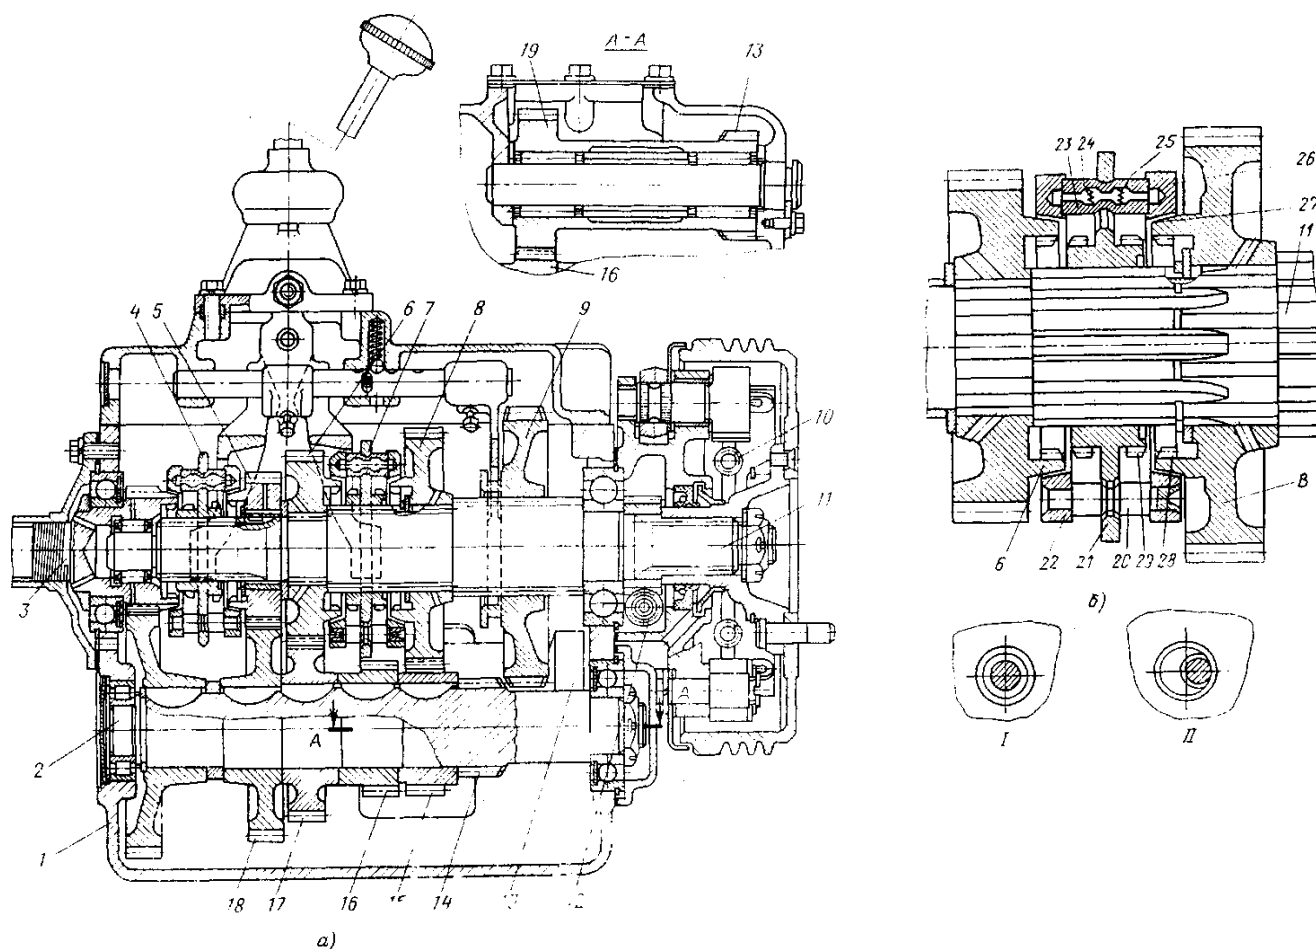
Коробка передач автомобиля ЗИЛ-130: а – общий вид; б – синхронизатор; 1 – картер; 2 – промежуточный вал; 3 – ведущий вал; 4 и 7 – синхронизаторы; 5 и 18 – зубчатая пара четвертой передачи; 6 и 17 – зубчатые колеса третьей передачи; 8 и 15 – зубчатые колеса второй передачи; 9 – колесо-каретка первой передачи и передачи заднего хода; 10 – стояночный тормоз; 11 – ведомый вал; 12 – шестерня привода спидометра; 13 и 19 – блок зубчатых колес второй передачи; 14 – шестерня первой передачи;
